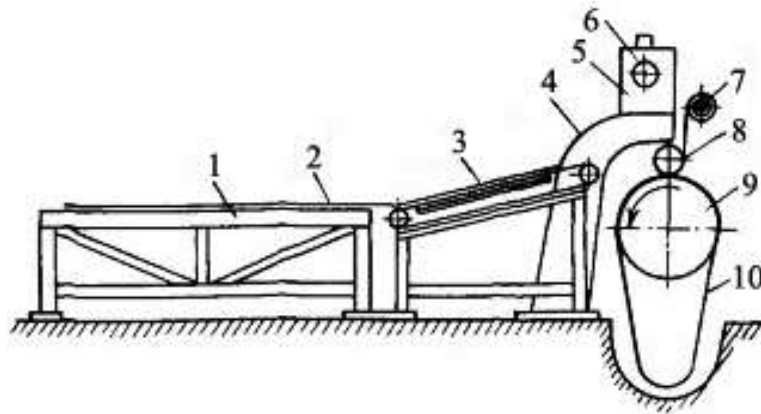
Схема роликового верстата для виготовлення браслетів:
